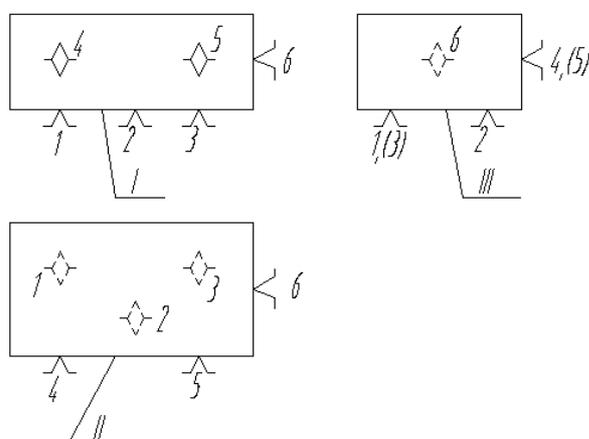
Схема базирования призматической детали. *I, II, III* - базы детали; 1...6 - опорные точки
